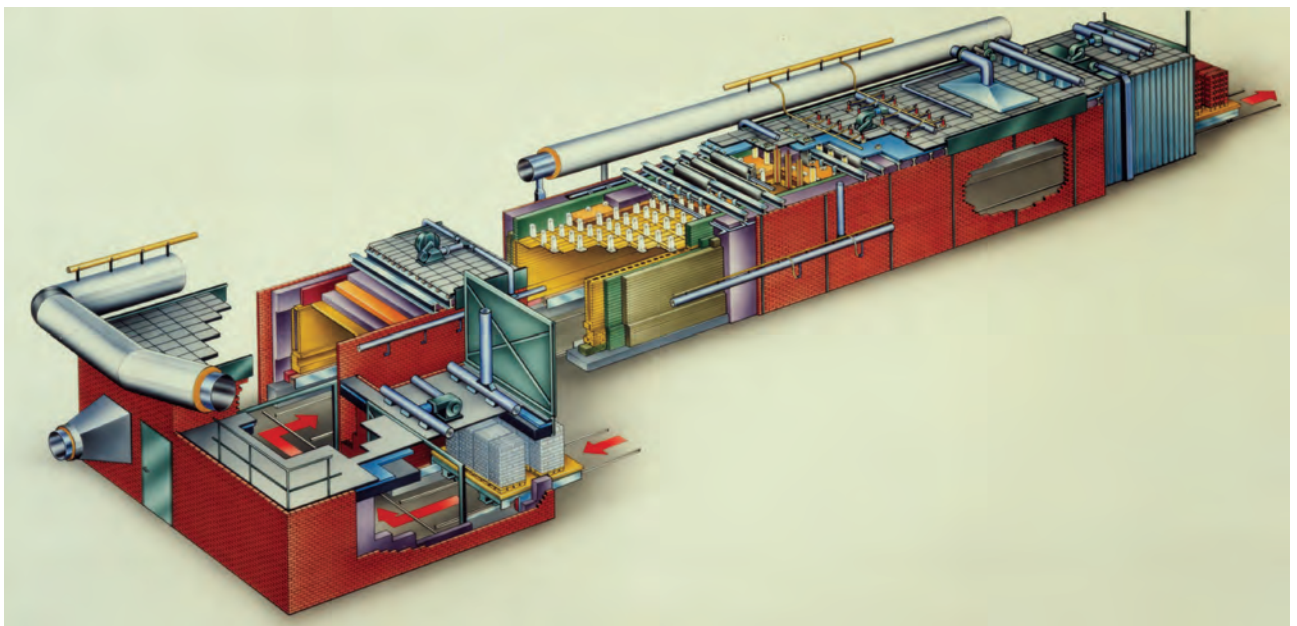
Tunnelofen mit Vorwärmer und geschlossener Umfahrt, Ofenkörper zum Teil in konventioneller Mauerwerksausführung
